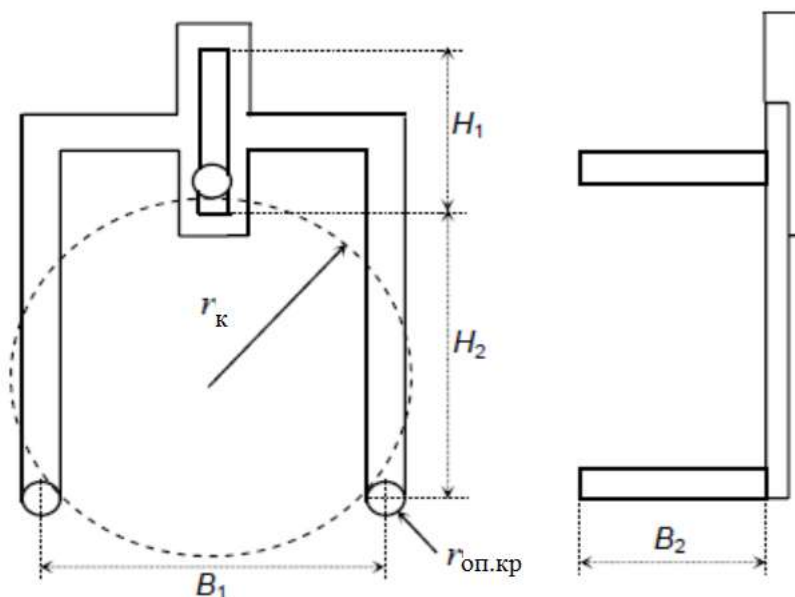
Схема геометричних розмірів, які визначають, з якими колесами може працювати інструмент.
